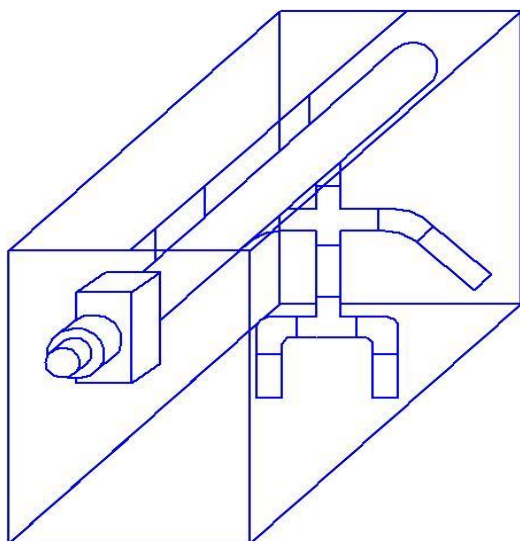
Общий вид сушильной камеры СЗО пожарного
